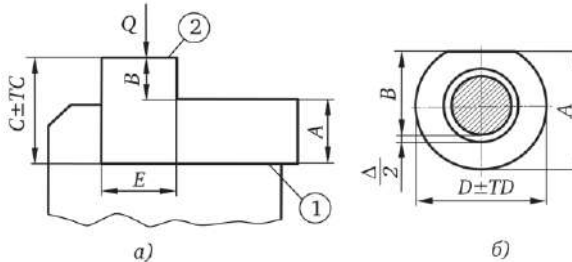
Схеми визначення похибки базування (Q — сила затиску)
